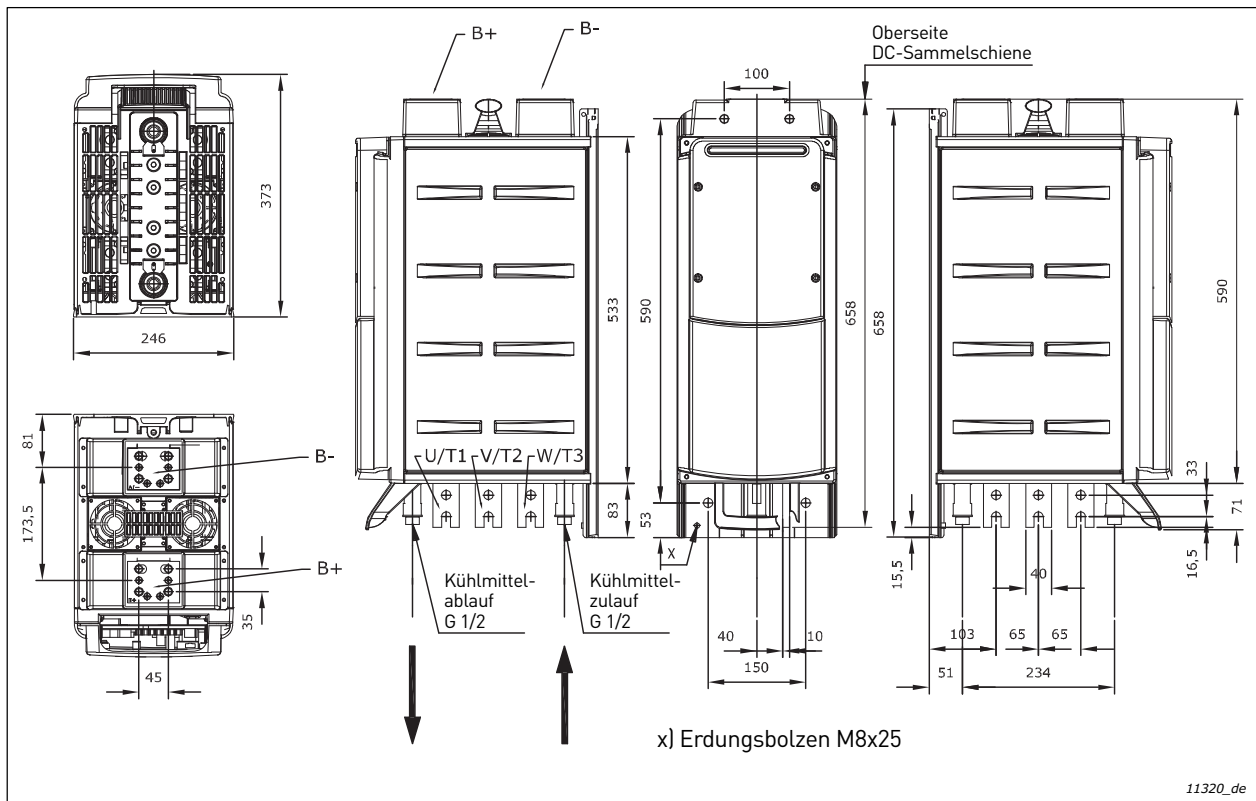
Flüssiggekühlter VACON®-Wechselrichter (CH61)
